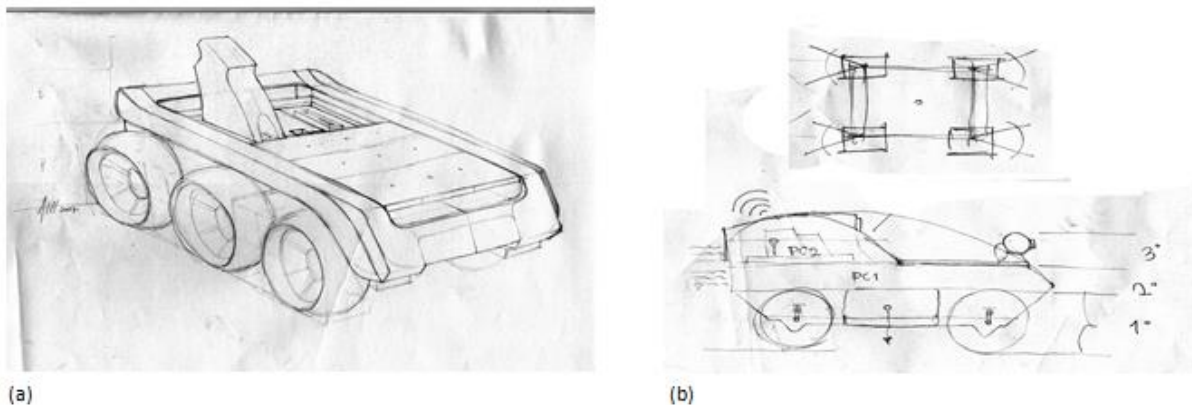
(a) Esboço inicial com seis rodas. (b) conceito com quatro rodas do RoboDeck
